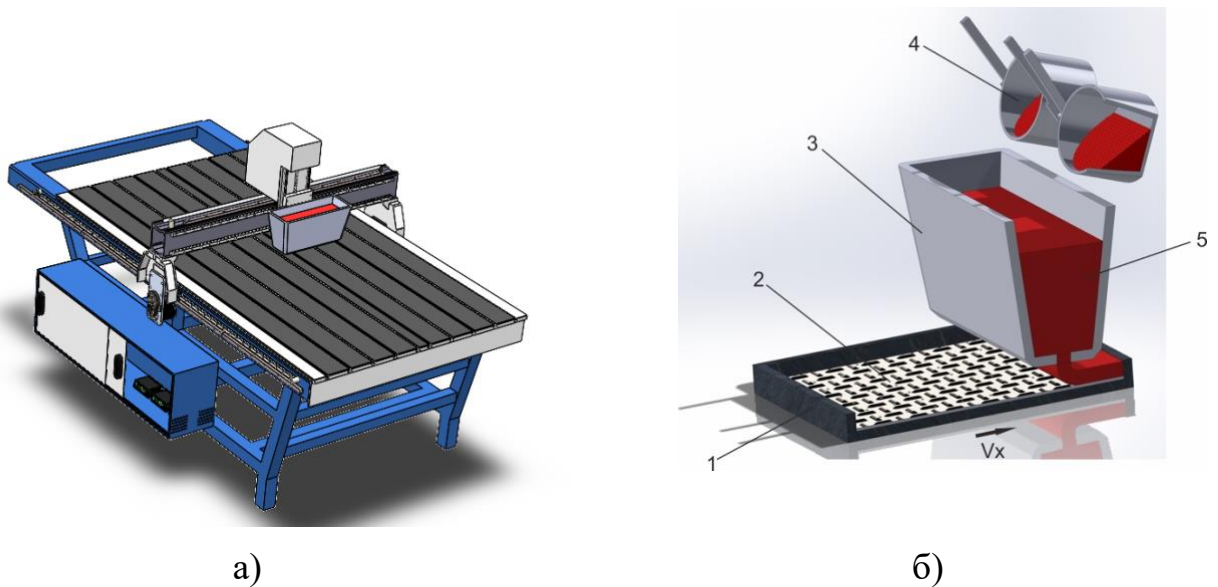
Комбінована установка з ливарним модулем (а) та схема формування біметалічного з'єднання (б): 1 — функціональний компонент; 2 — лазерний макрорельєф; 3 — щілинна фурма; 4 — подача розплаву з індукційної печі; 5 — конструкційний метал. Стрілкою V_x позначено вектор контрольованого руху заливки.
